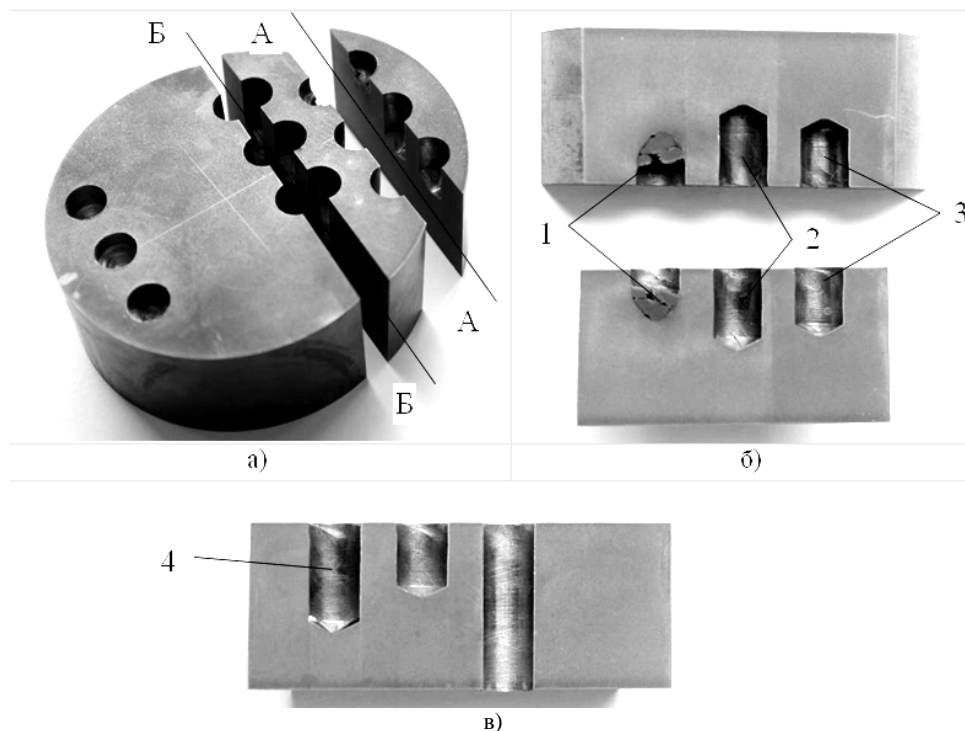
Заготовка из сплава BT22 после экспериментального сверления:
